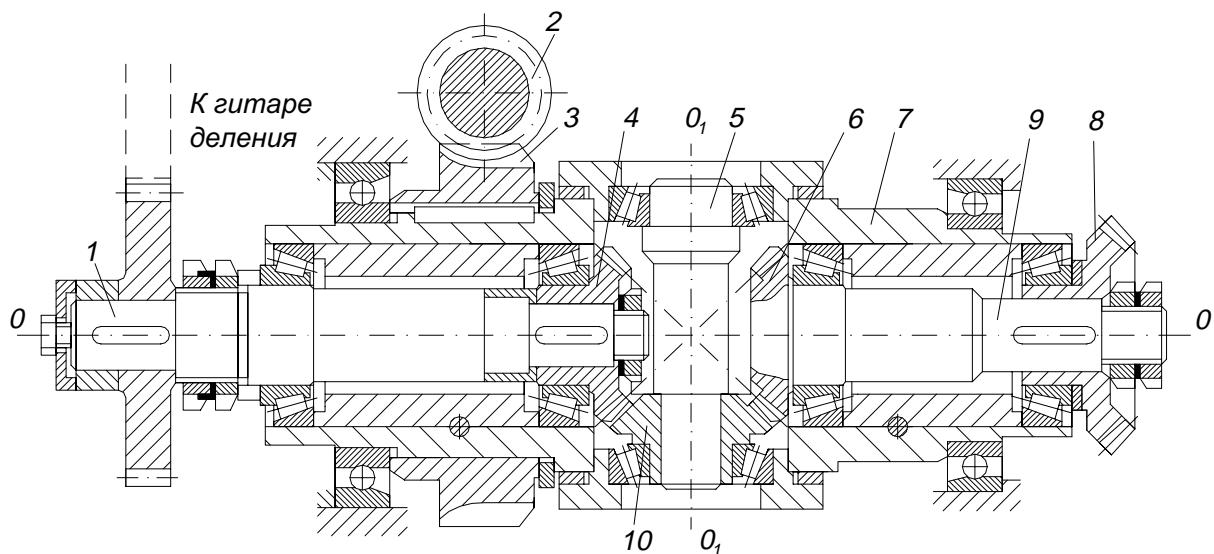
Дифференциал зубофрезерного станка мод. 5К32
